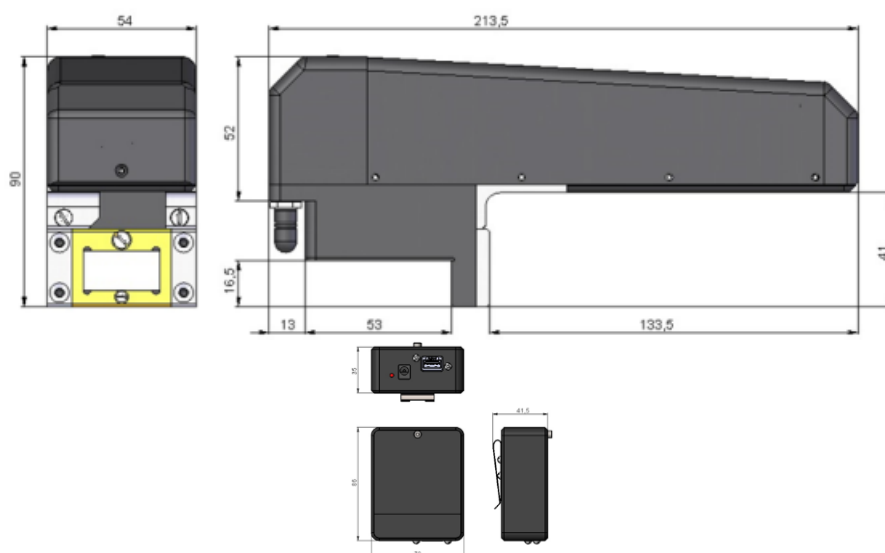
Dimensões scanner super compacto Bateria Externa (SSEB) orientativas
